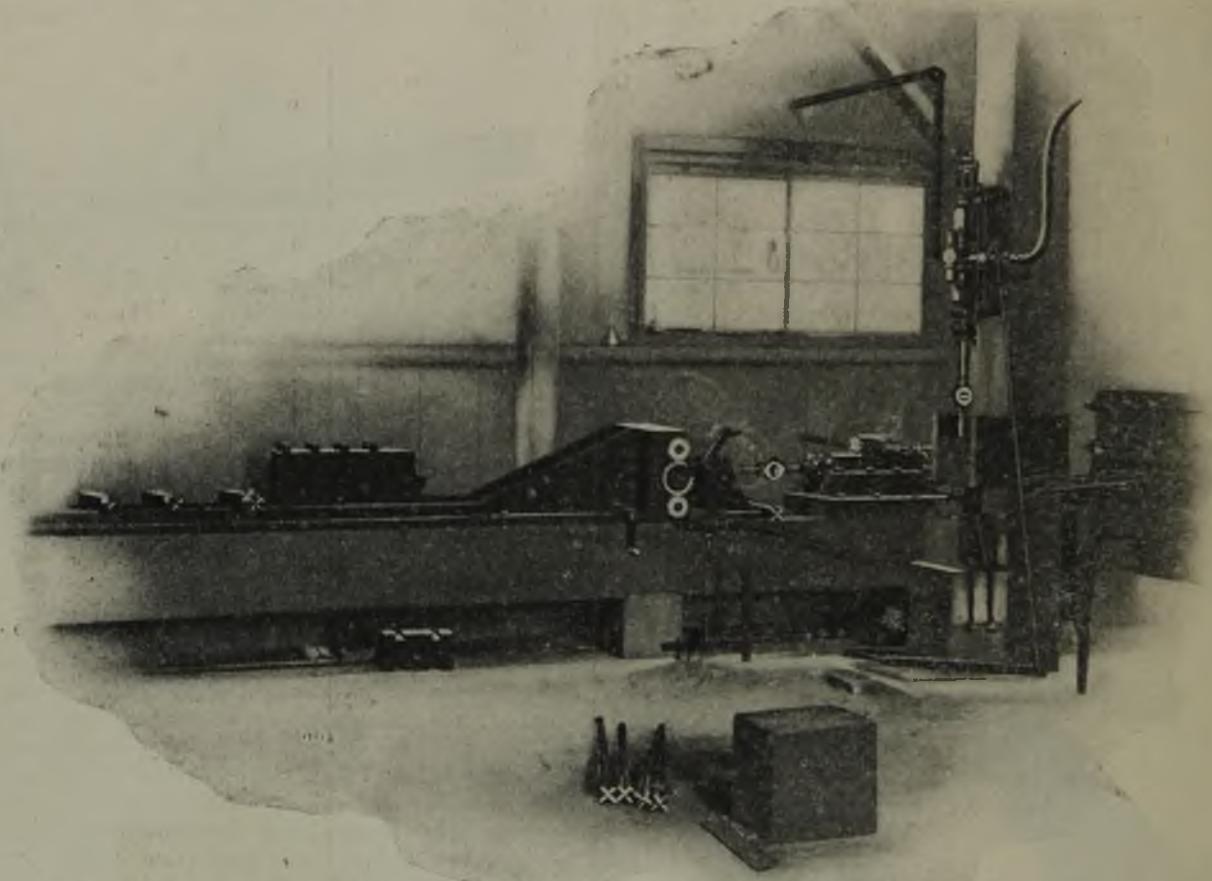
Schmiedemaschine für Bohrmeißel. Ingersoll-Rand Drill Co., New York-Berlin.
